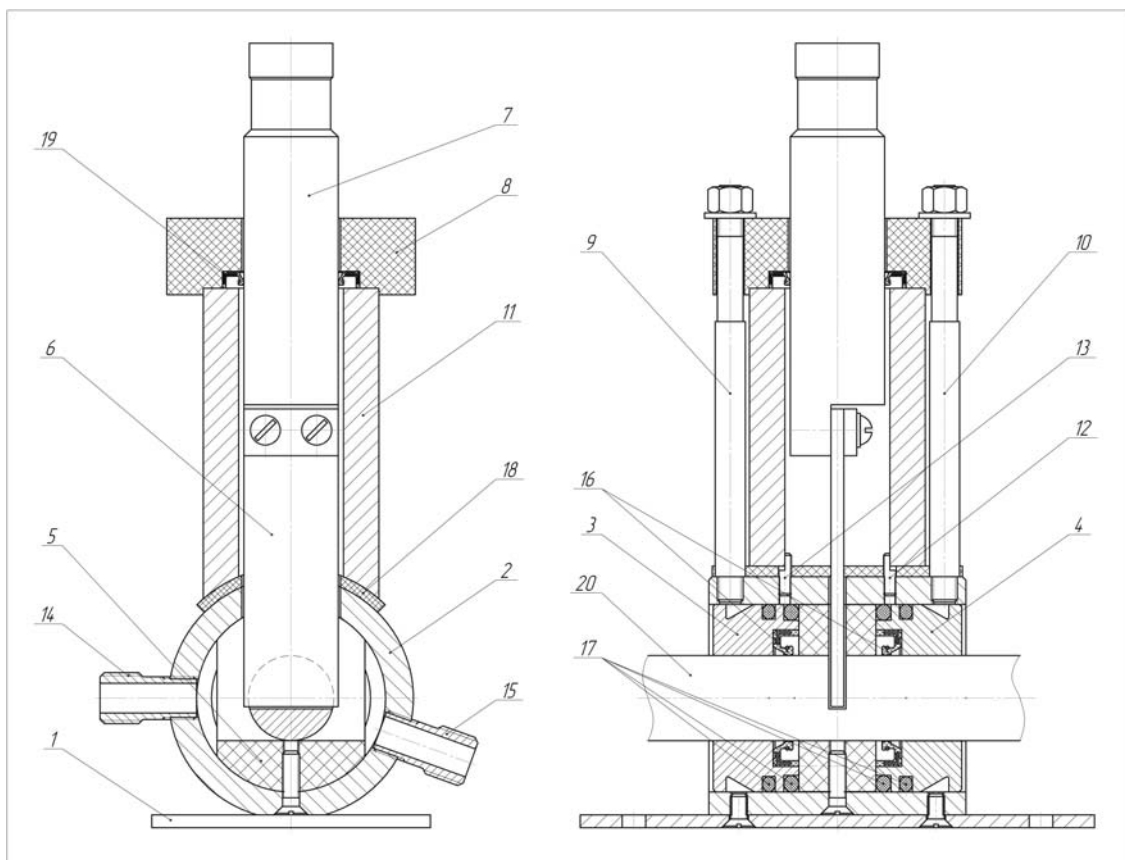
Пристрій для різання пруткового металу на мірні заготовки способом РОД
